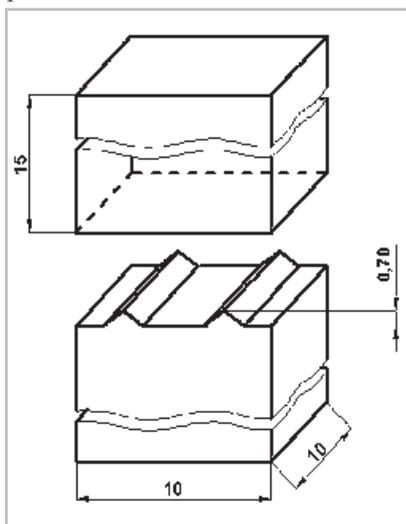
Чертеж экспериментального образца из жесткого полимера для ультразвуковой сварки.
